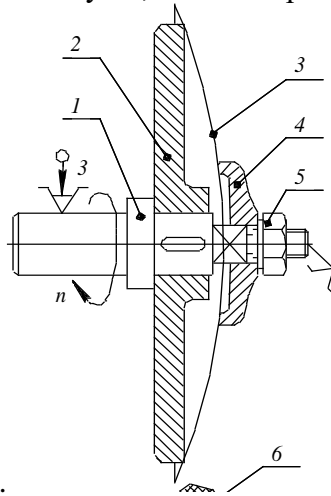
Схема заточування диска на токарно-гвинторізній верстаті:
